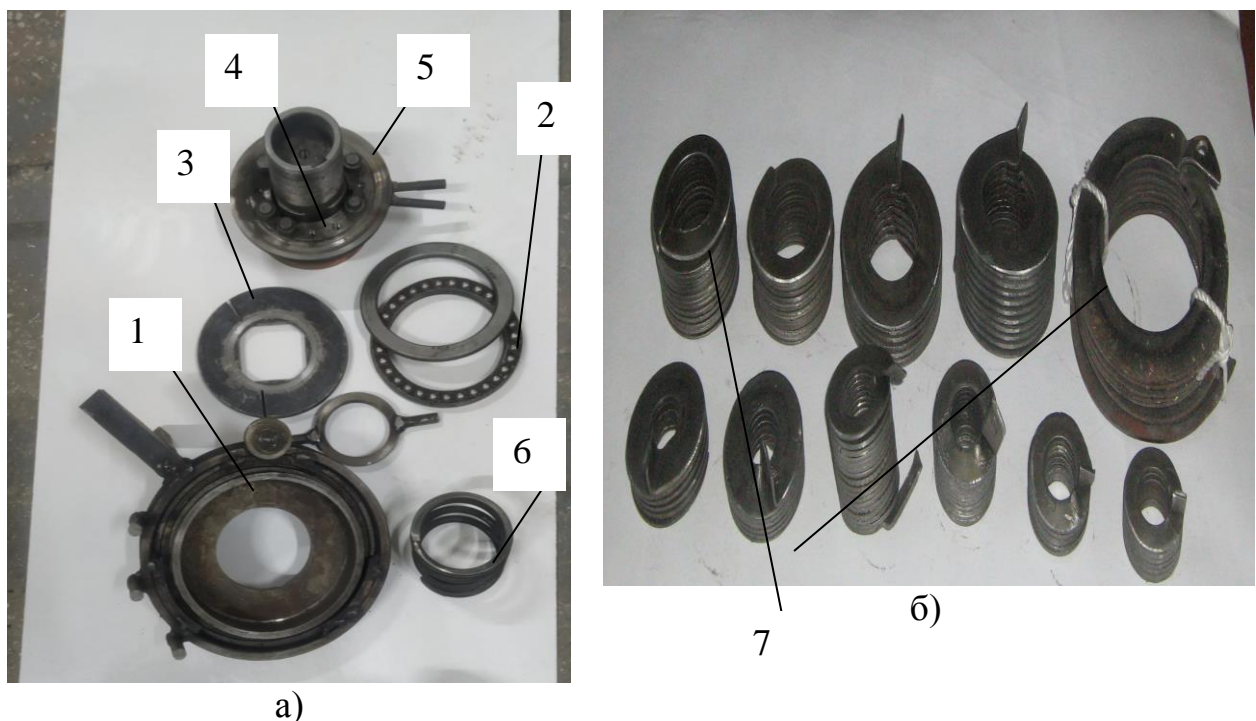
Загальний вигляд пристрою для технологічного процесу навивання гвинтової заготовки з обертовою втулкою у розібраному вигляді – а) навиті гвинтові заготовки - б) : 1 – зовнішня обойма; 2 – підшипник; 3 – кільце; 4 – направляючі втулки; 5 – внутрішня обойма; 6 – пружина; 7 – гвинтова заготовка
